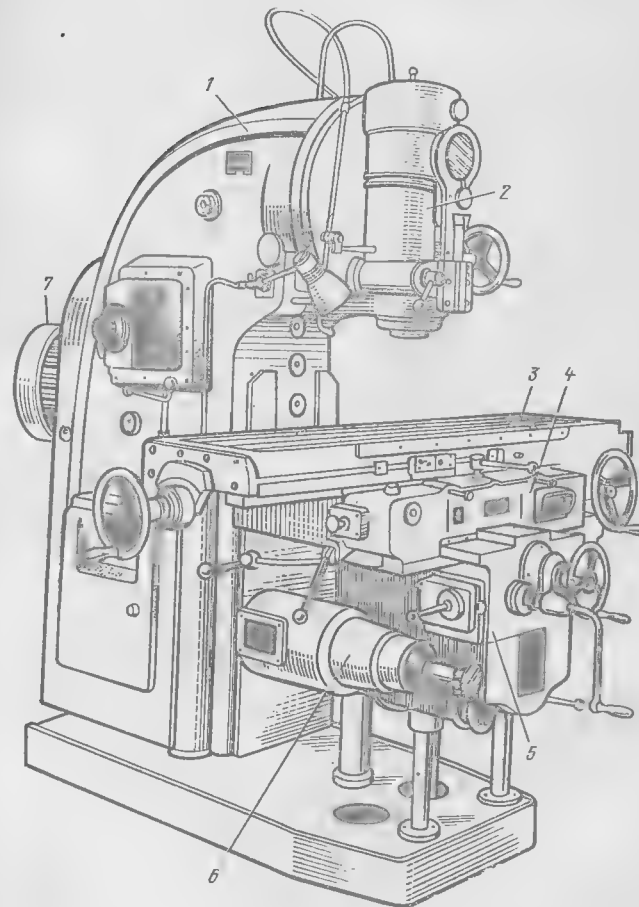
Вертикально-фрезерный станок модели 6Н13.
